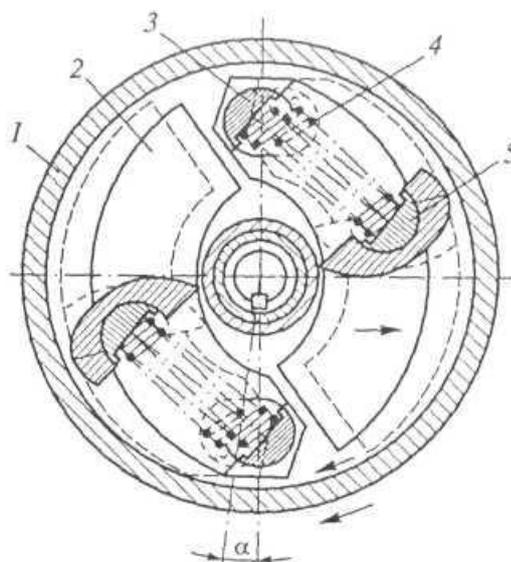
Муфта опережения впрыска топлива: 1 - корпус; 2 - груз; 3 - ось; 4 - пружина; 5 - проставка; α - угол опережения впрыска топлива
